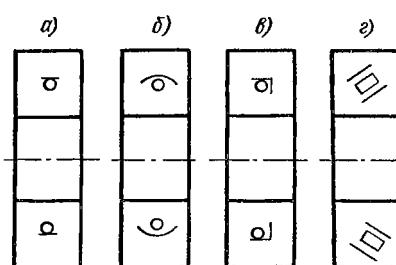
Условное изображение подшипника с указанием типа: а – радиальный шариковый однорядный; б – радиальный шариковый самоустанавливающийся (сферический); в – радиально-упорный шариковый однорядный; г – радиально-упорный роликовый однорядный
